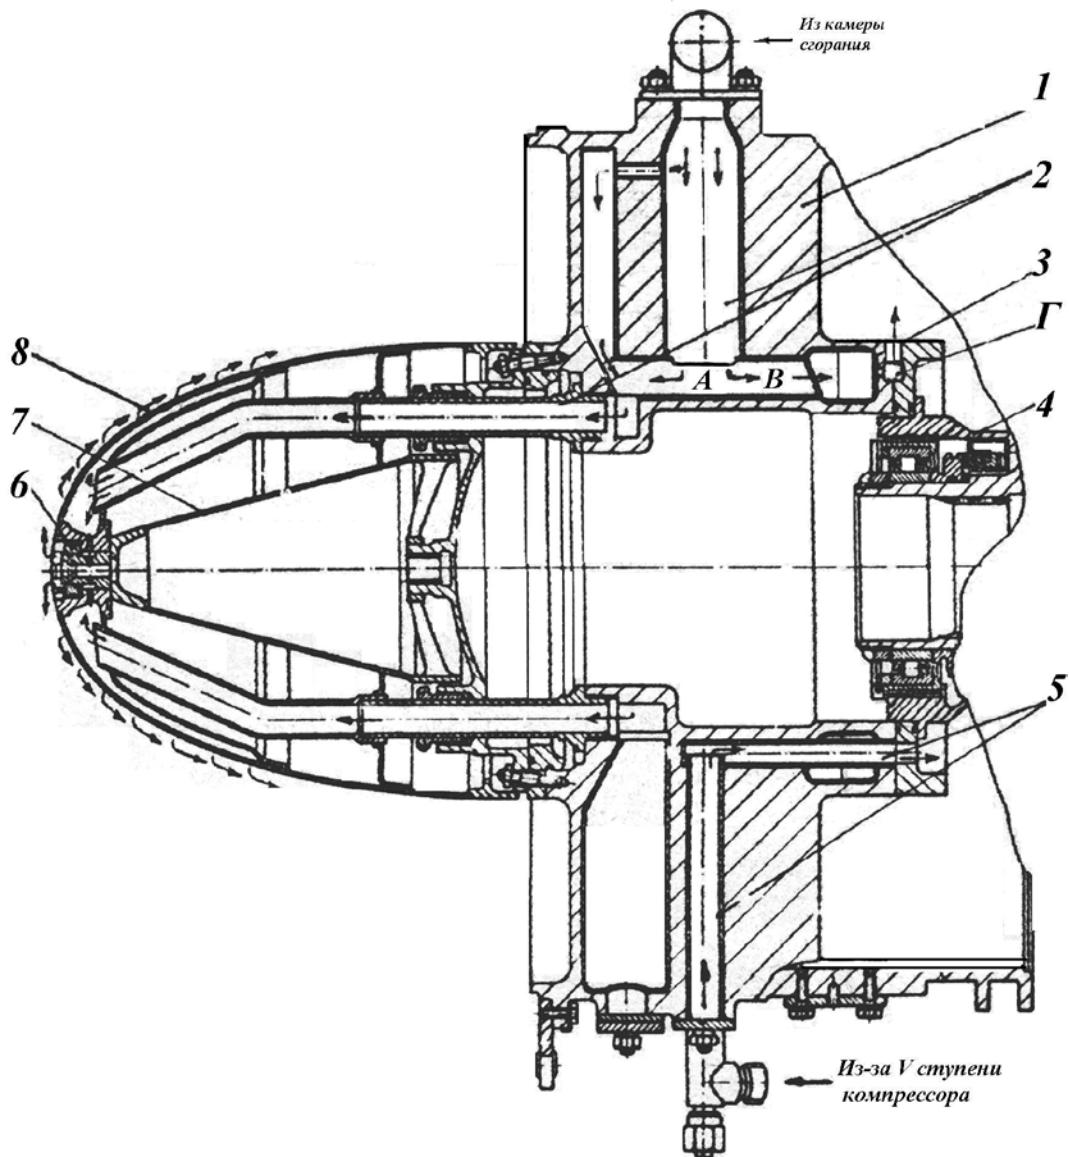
Обогрев элементов входного устройства компрессора:
